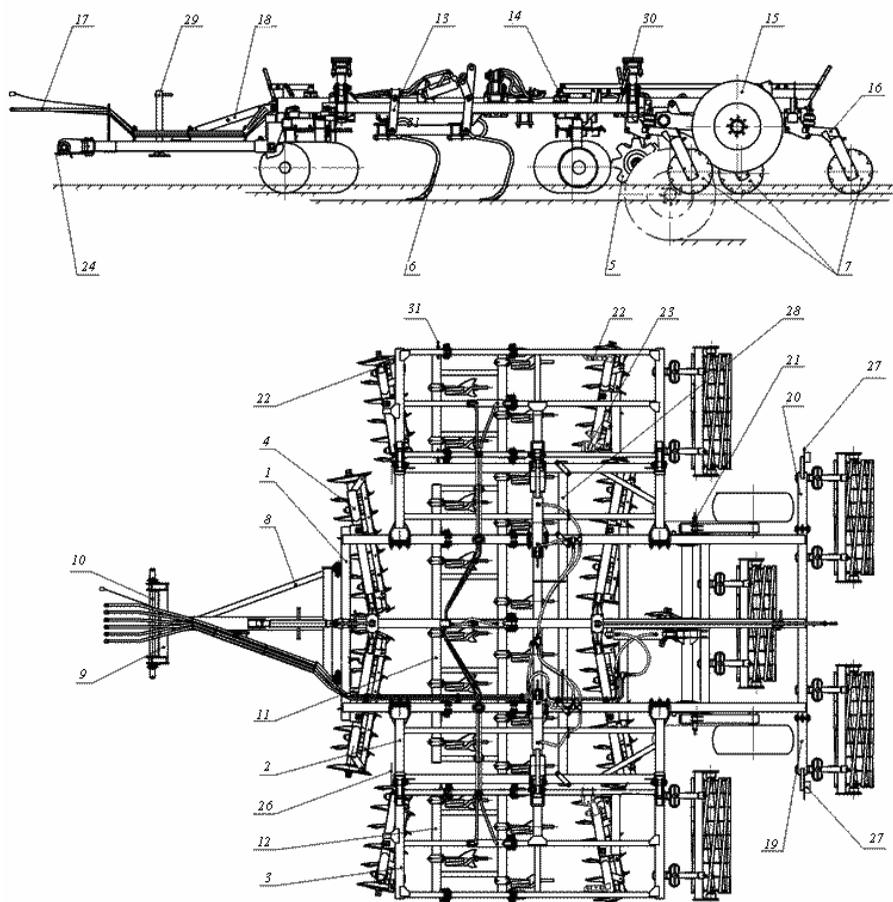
Агрегат комбинированный широкозахватный для минимальной обработки почвы АКМ-6:
